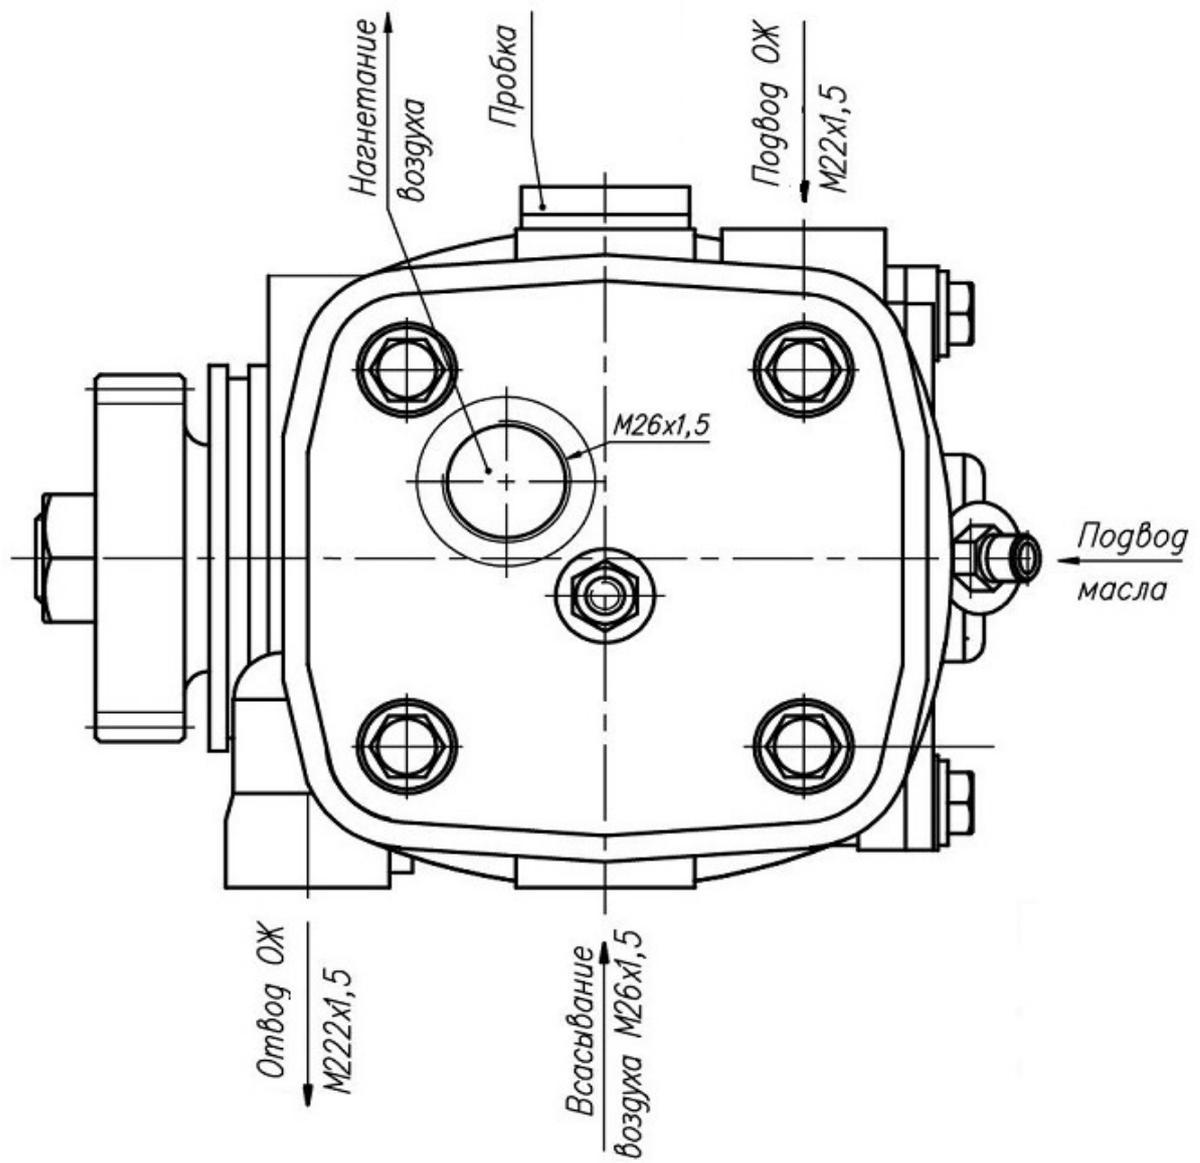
Расположение всасывающих и нагнетательных воздушных патрубков и отверстий подвода и отвода охлаждающей жидкости компрессора АМ.3509015-05.
